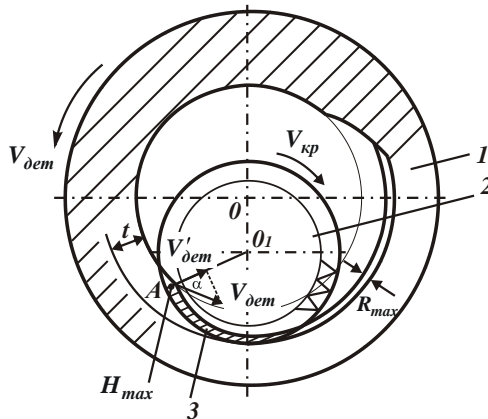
Розрахункова схема параметра шорсткості під час внутрішнього шліфування: 1 – деталь; 2 – круг; 3 – форма зрізу окремим зерном круга
